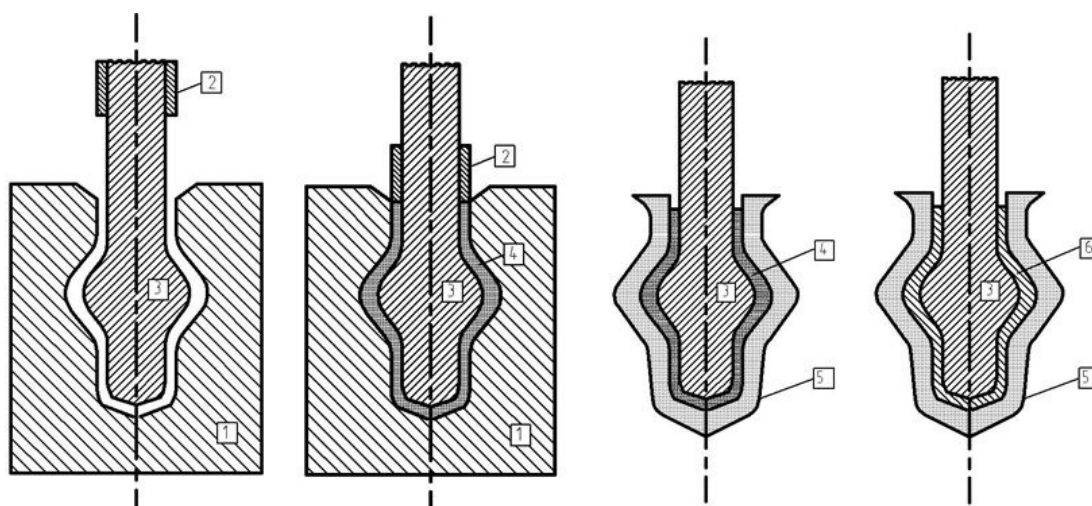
Схема последовательности формирования биметаллической отливки: 1 – пресс-форма; 2 – подвижный пресс-пуансон; 3 – стальной каркас; 4 – воскообразный напрессованный слой; 5 – керамическая оболочка; 6 – биметаллическая отливка в оболочковой форме.
